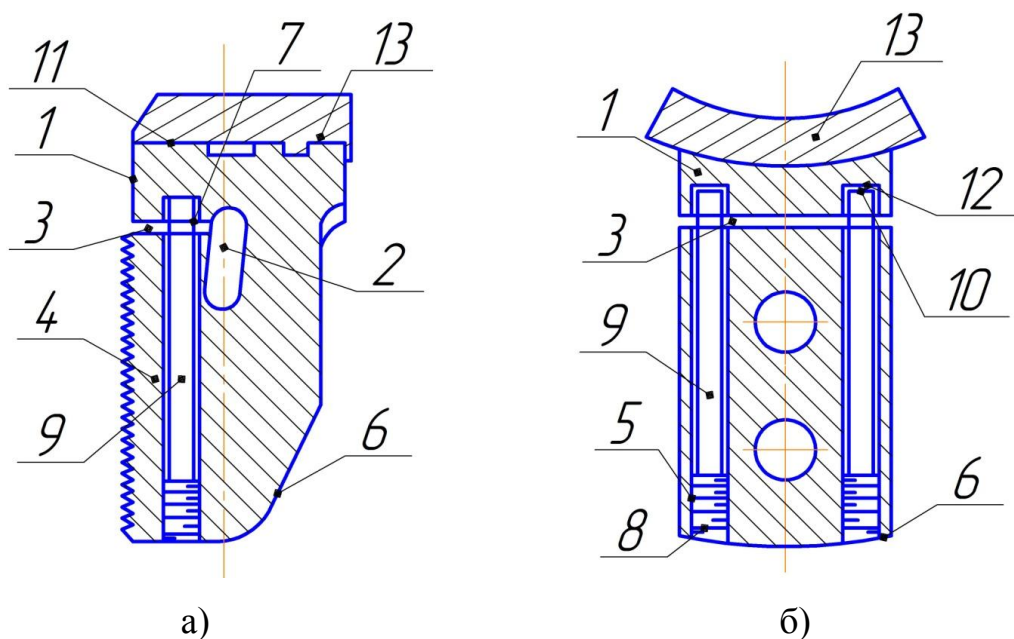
Адаптивний кулачок з вставками в розрізі
